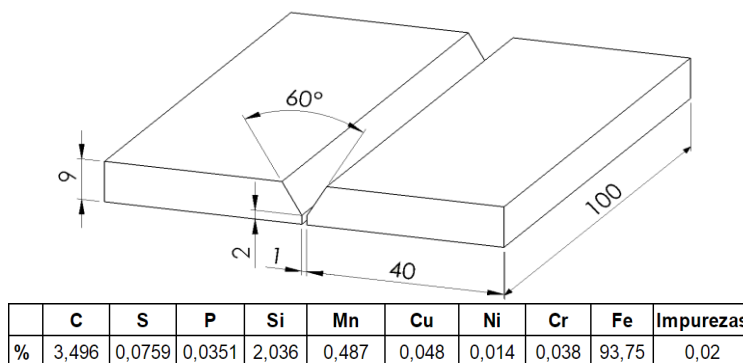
Dimensões (em milímetros) das amostras e tipo da junta soldada.
